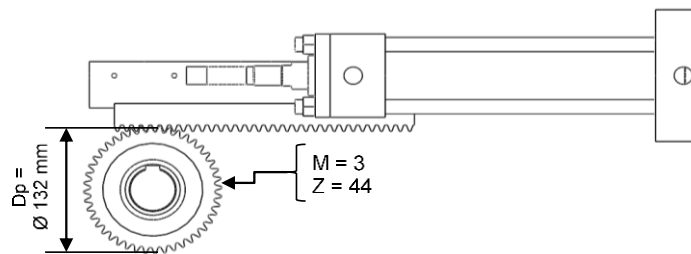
DIMENSÃO DA ENGRENAGEM
